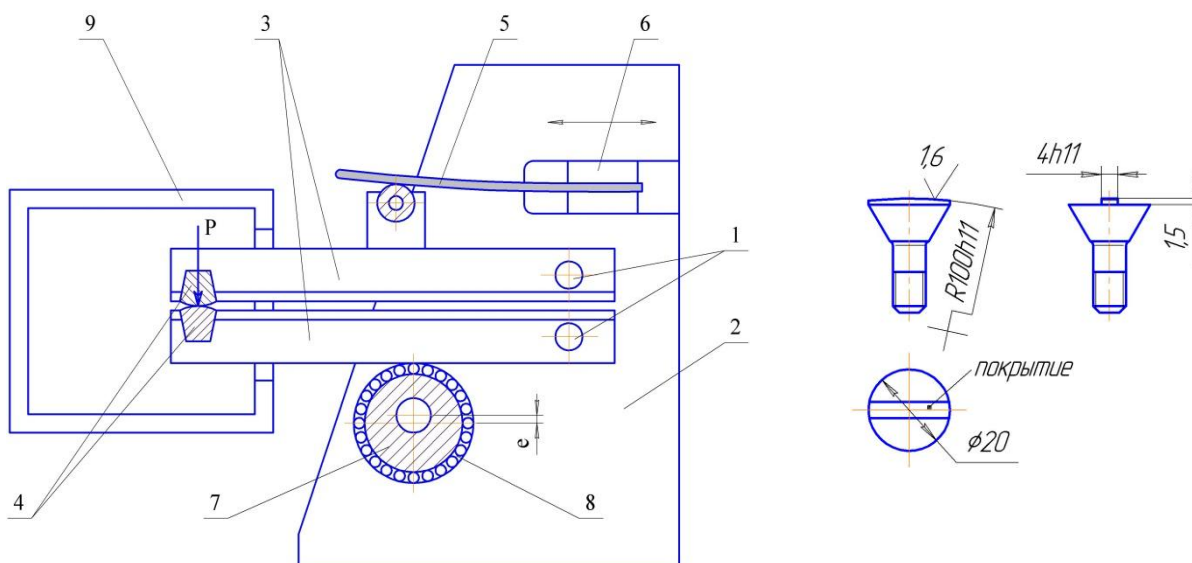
Машина трения и образец для испытания покрытий: 1- оси рычагов; 2- плиты корпуса установки; 3- рычаги; 4- испытуемые образцы; 5- плоская пружина; 6- узел перемещения пружины; 7- вал; 8- внешняя обойма подшипника; 9- объем моделирования среды трения.
